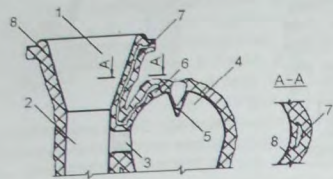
Разрез КО со щелевым выпором: 1 – ЛВ; 2 – стояк; 3 – литниковый ход; 4 – прибыль; 5 – стержень атмосферного давления; 6 – платик; 7 – выпор; 8 – КО
